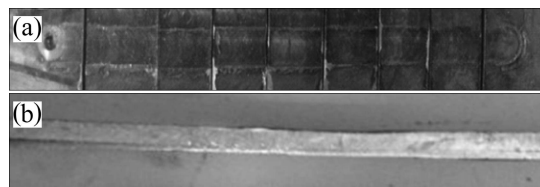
紫铜-不锈钢 FSW 焊缝的表面形貌
